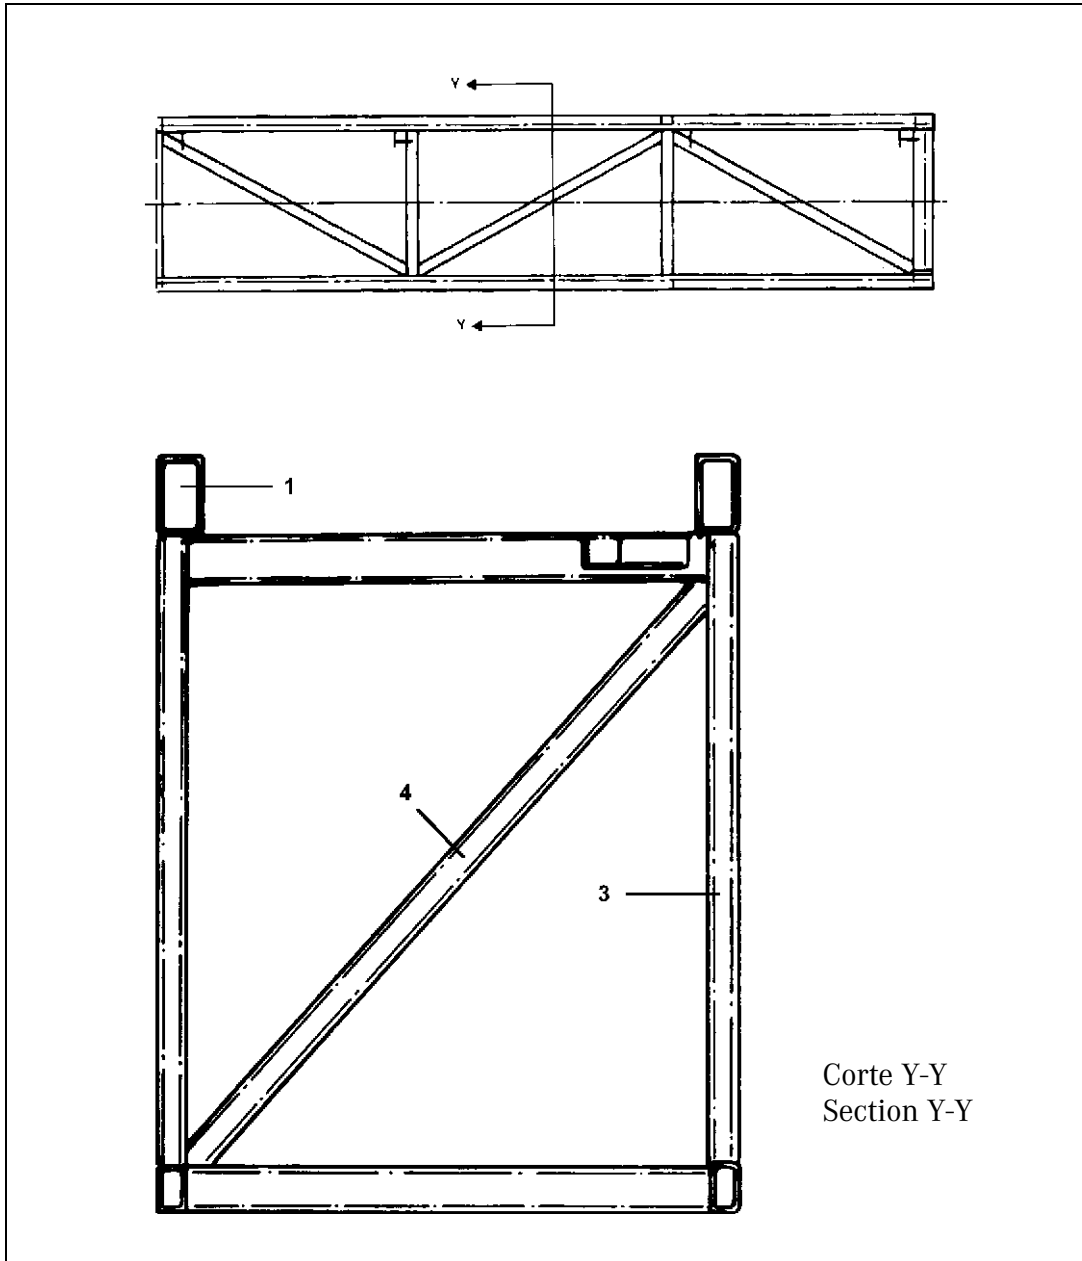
Detalle C - Vista superior de la estructura central reticulada, (ejemplo)
